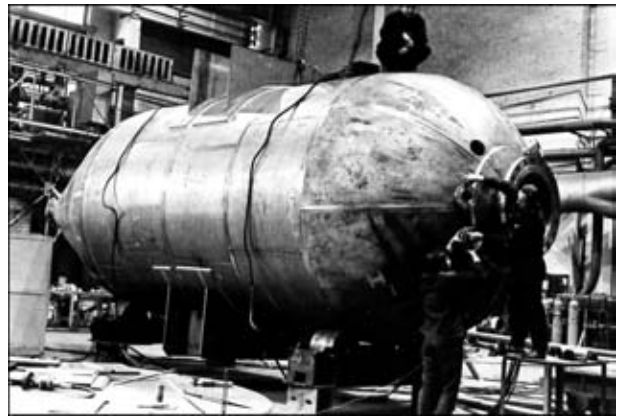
Изготовление гидролизного аппарата из сплава АТЗ с толщиной корпуса 24 мм
